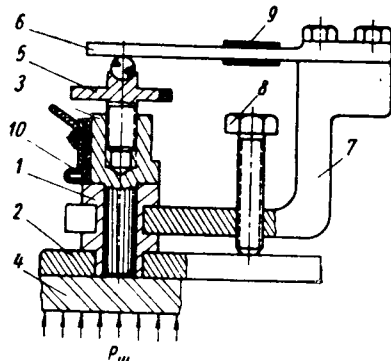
Общий вид датчика прибора для определения давлений на обод колеса.
